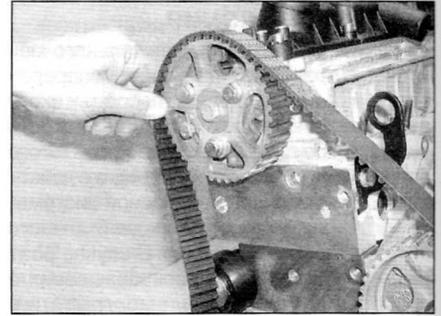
, в. ...зубчатый шкив распределительного вала...
